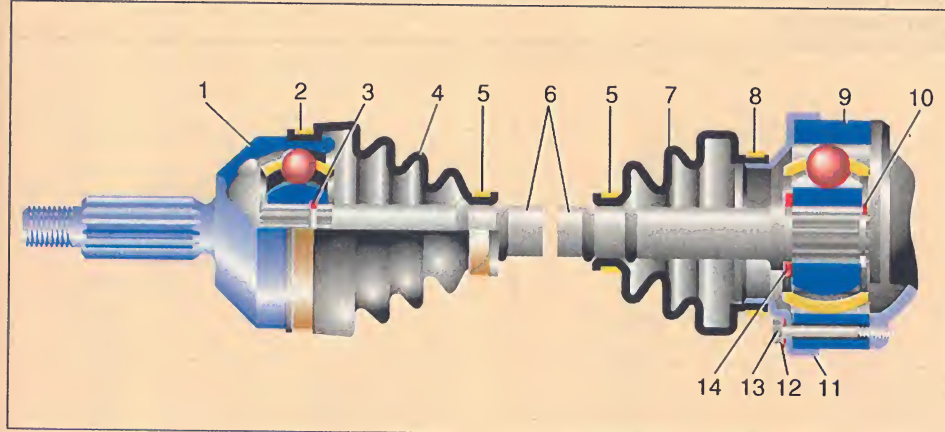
Привод переднего колеса АЗЛК-2141 в сборе: 1 - корпус наружного шарнира; 2, 5, 8 - хомуты чехлов; 3, 10 - запорные кольца; 4, 7 - чехлы; 6 - вал привода колеса; 9 - внутренний шарнир; 11 - держатель чехла; 12 - пластина; 13 - винт; 14 - упорное кольцо.
